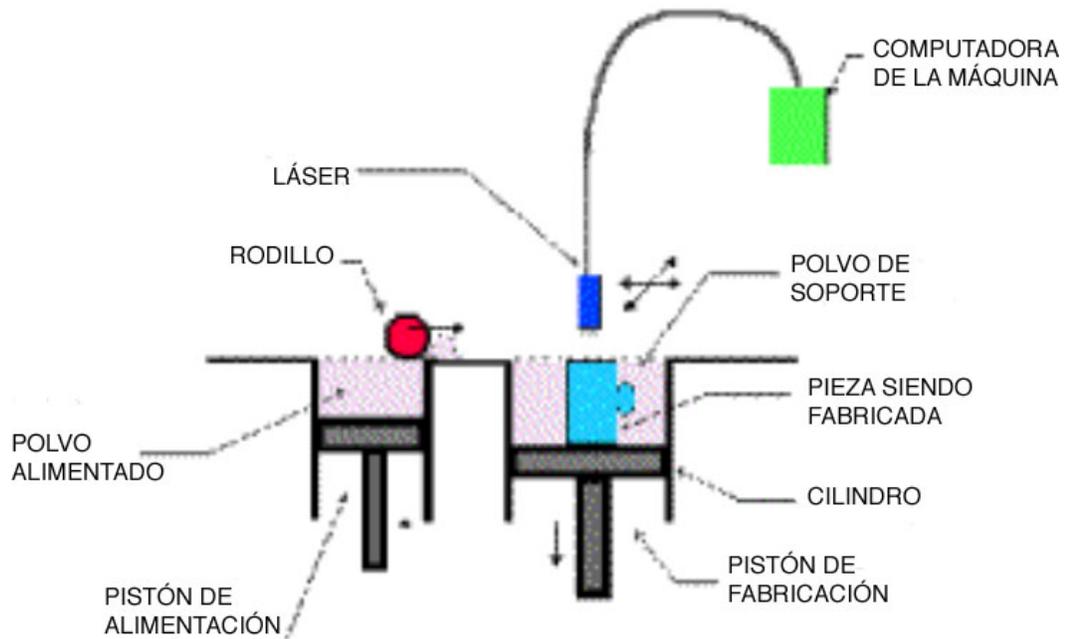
Técnica de Impresión 3D (3DP)
